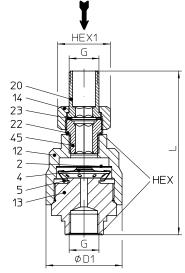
9 Eingang: Gewindezapfen, Ausgang: Gewindemuffe
